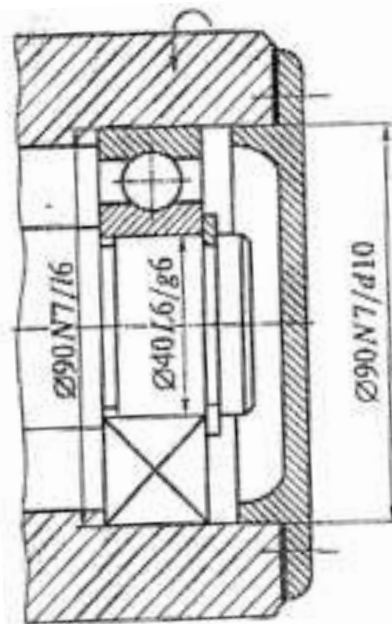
Обозначение посадок в подшипниковых узлах.
